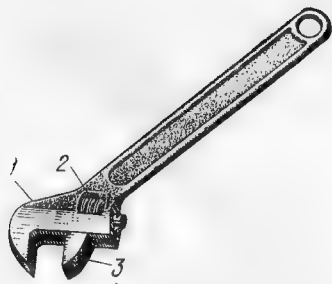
1 — корпус; 2 — червяк; 3 — губка подвижная с рейкой
